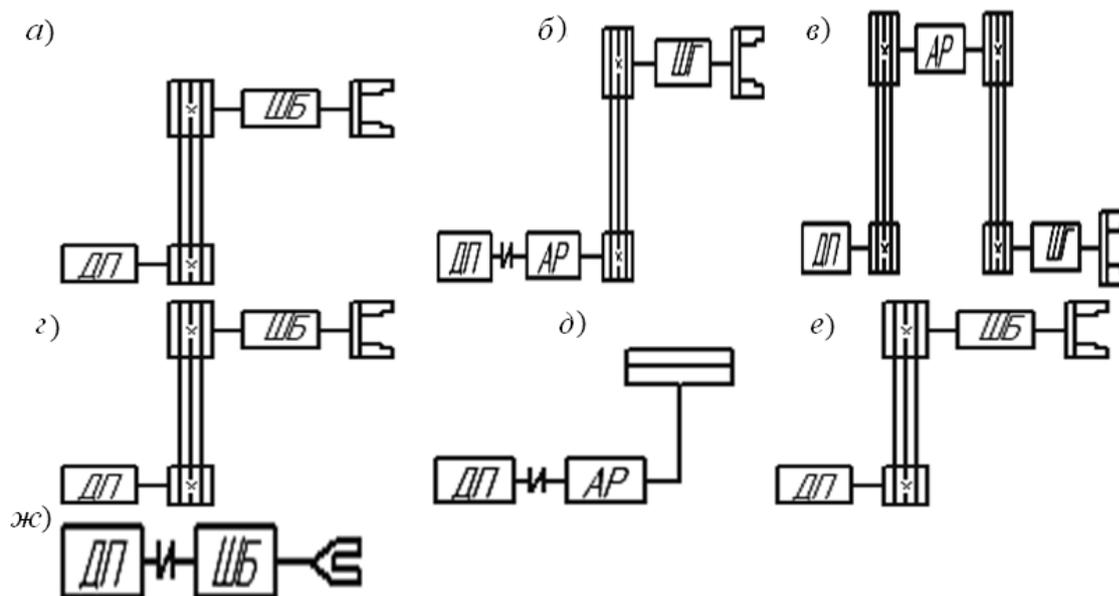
Типовые структуры главного привода станков с ЧПУ
